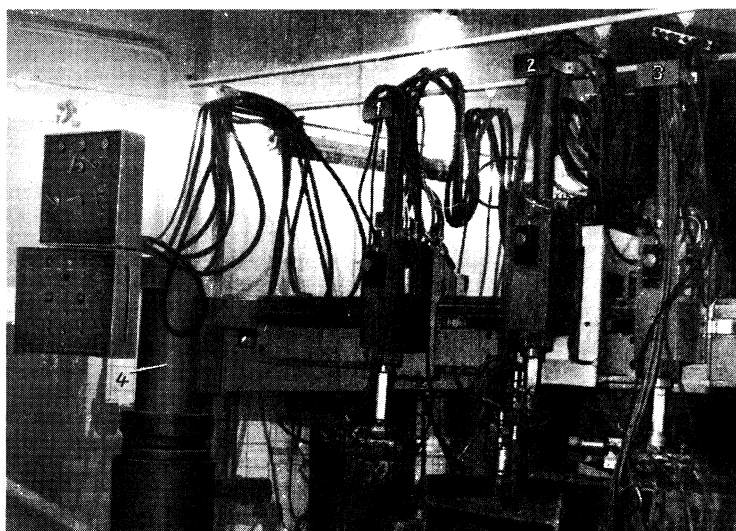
Машина для резки прокатных и сварных балок:
